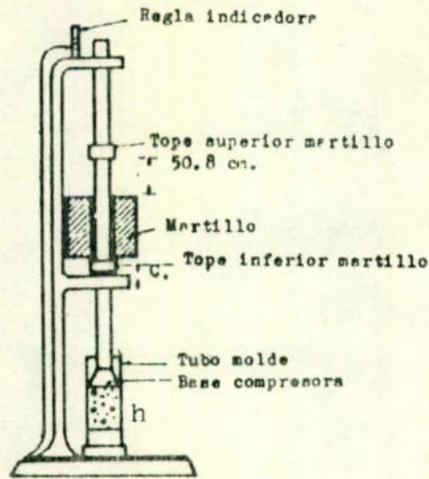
Esquema del aparato para fabricar probetas estándar para ensayos de masas de moldeo.
